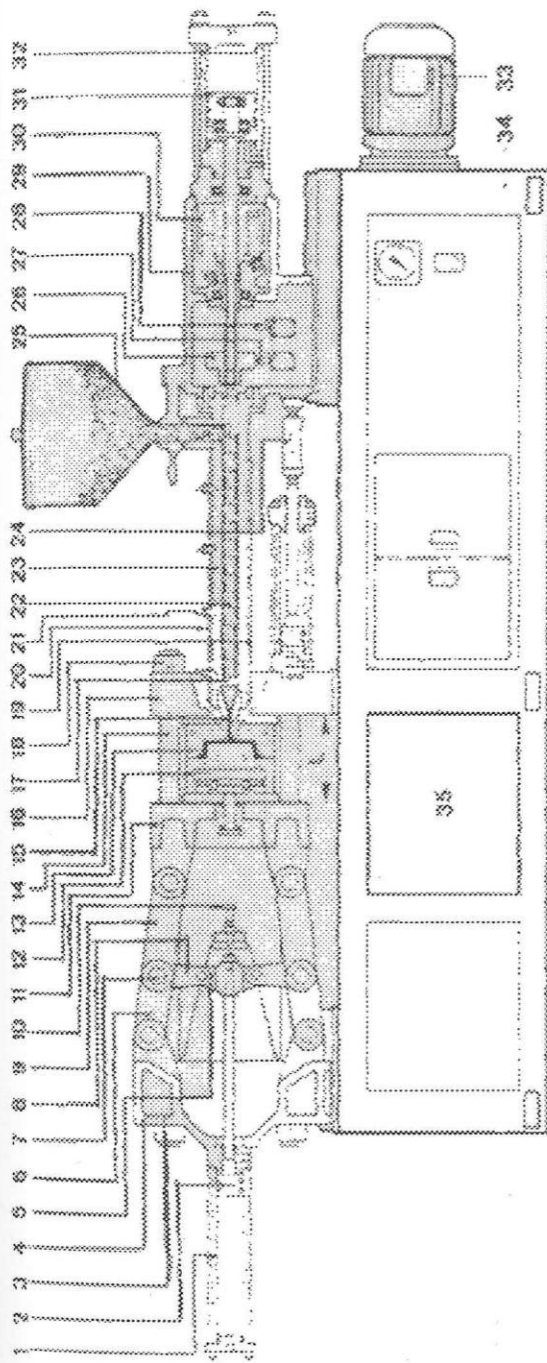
SECCIÓN LONGITUDINAL DE UNA MÁQUINA DE MOLDEO POR INYECCIÓN POR HUSILLO RECIPROCANTE, DEL TIPO DOBLE RODILLERA. Nótese el molde cerrado y el husillo (22) en posición al final de la inyección.
